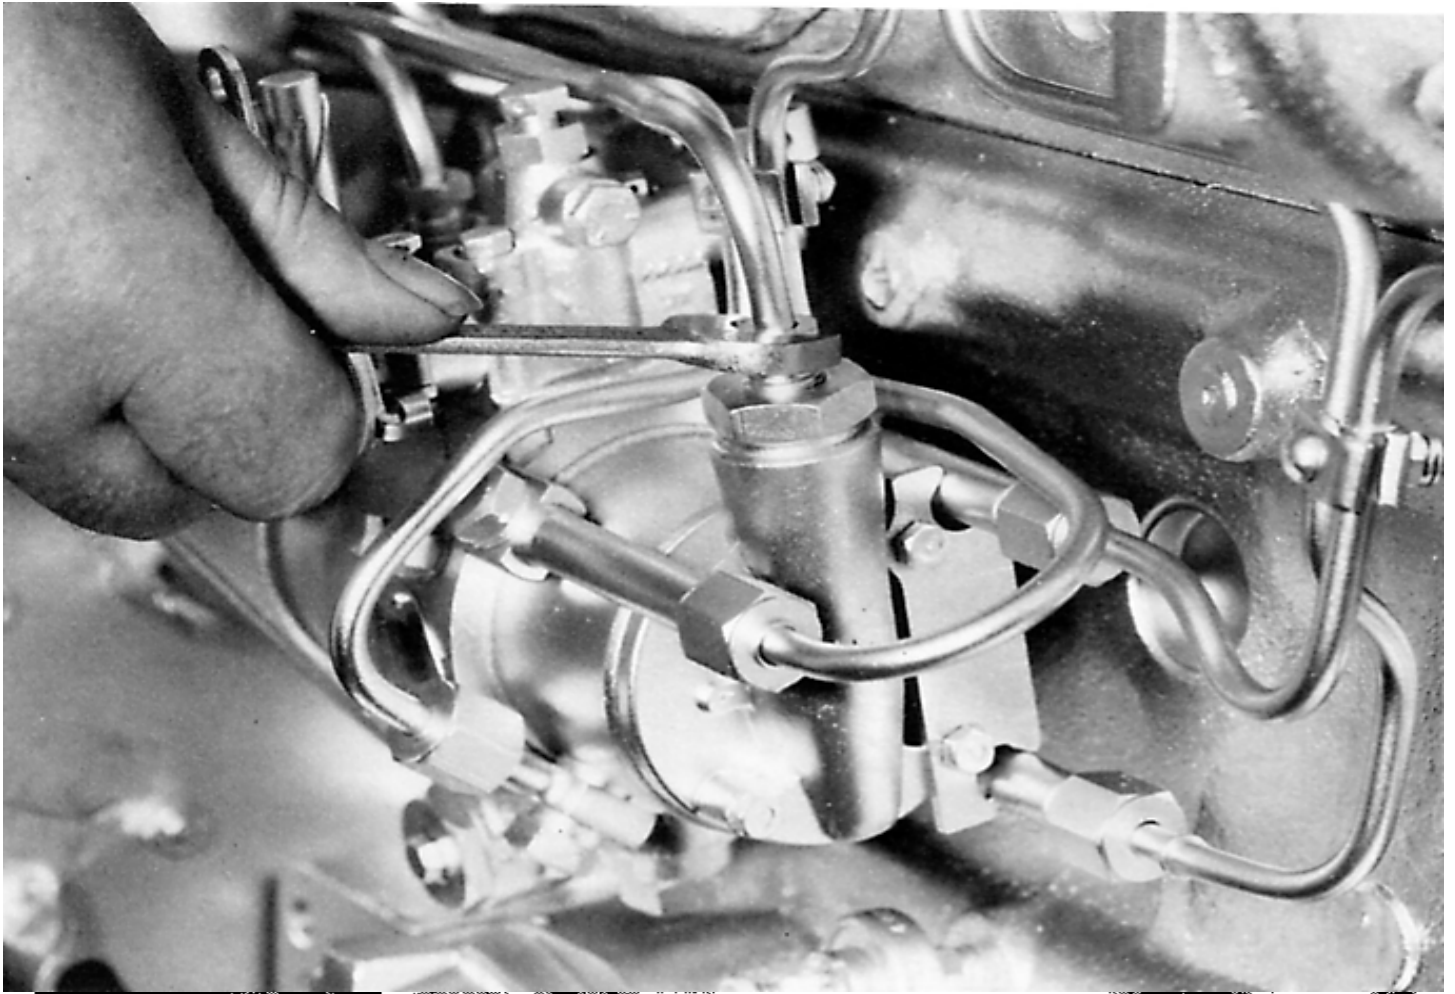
Desserrage du raccord d'arrivée de gazole à la pompe d'injection (Purge 4).
